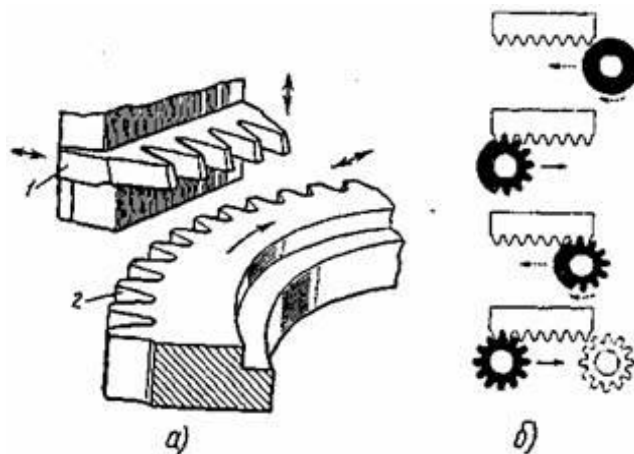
Схема нарезания зубьев зубчатой гребенкой
